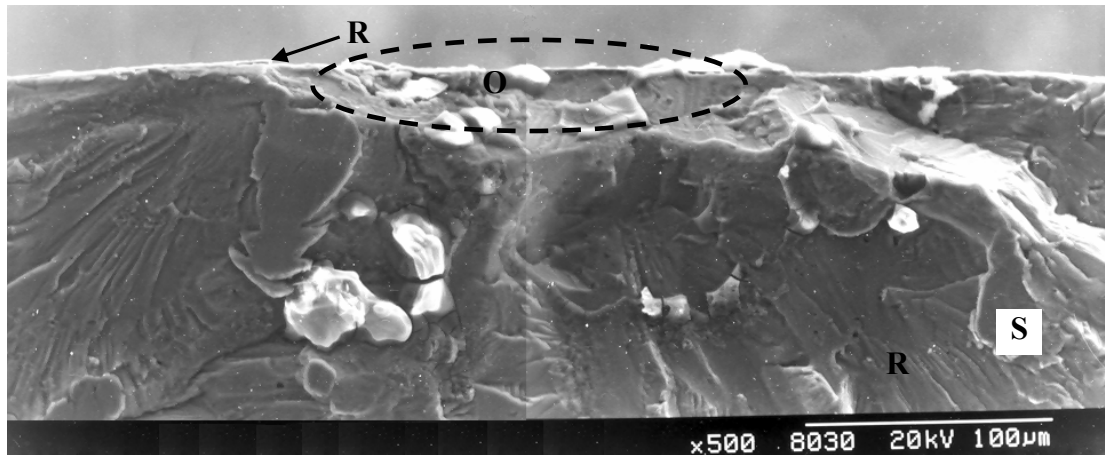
Detalle del inicio de grieta en superficie de fractura de la probeta N° 3
